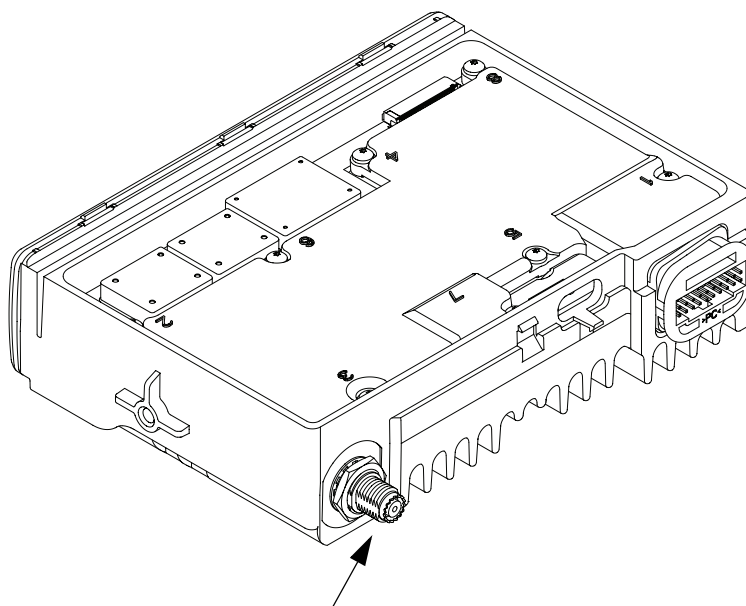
Ordre de serrage des vis pour fixer la plaque de protection moulée
